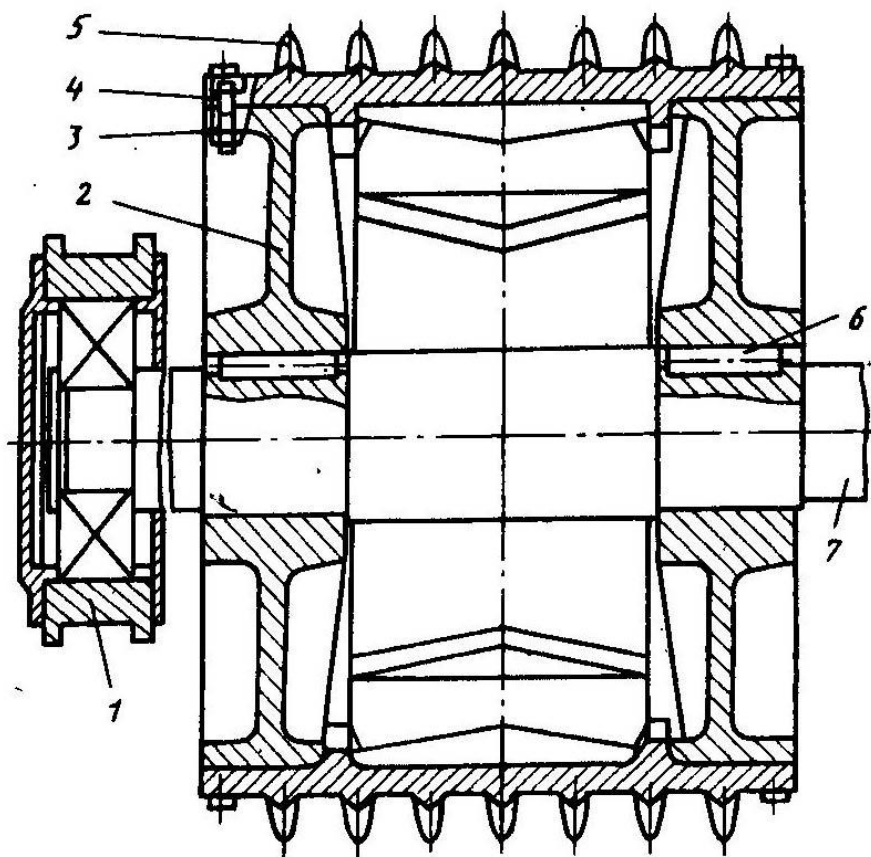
Валок двухвалковой зубчатой дробилки СМД-175А
